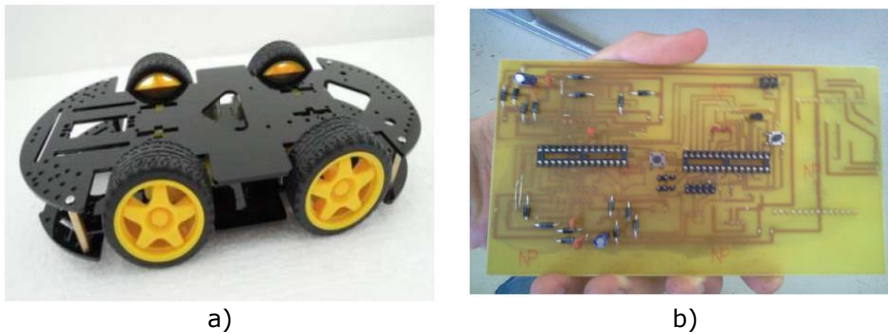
a) Demonstratorul mecatronic; b) Placa de circuit PCB [Sandru, 2015]
